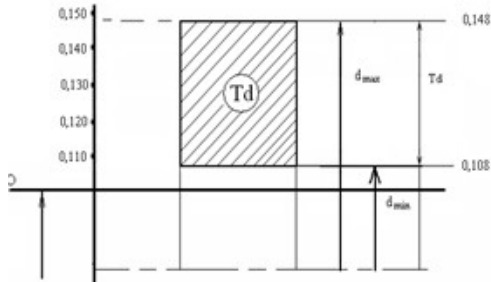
Схема расположения поля допуска вала
